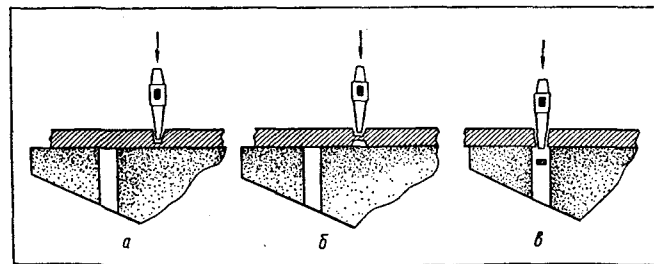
Пробивка с предварительным уплотнением металла (а, б, в — последовательность операций)
